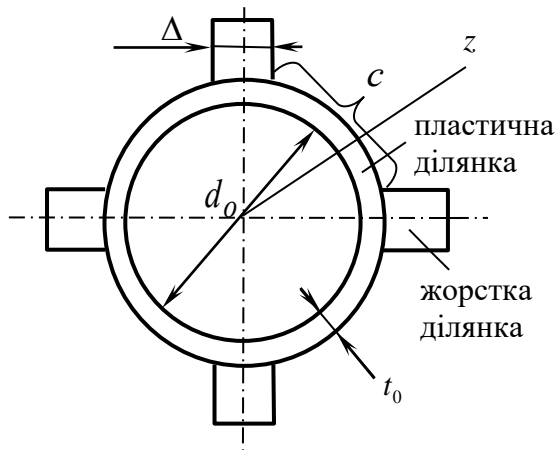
Заготовка із жорсткими та пластичними ділянками.
